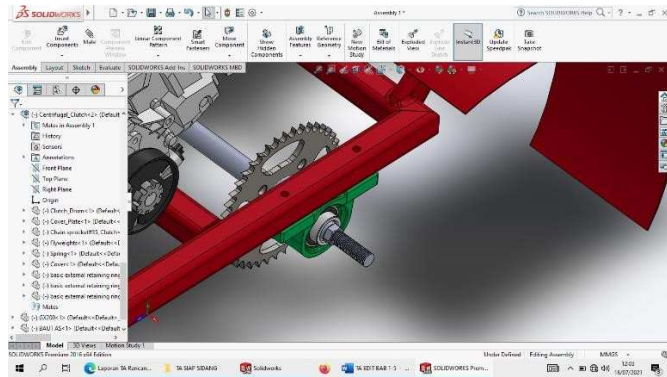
150 Hasil *Assembly* Mesin Penggerak dan Kerangka
